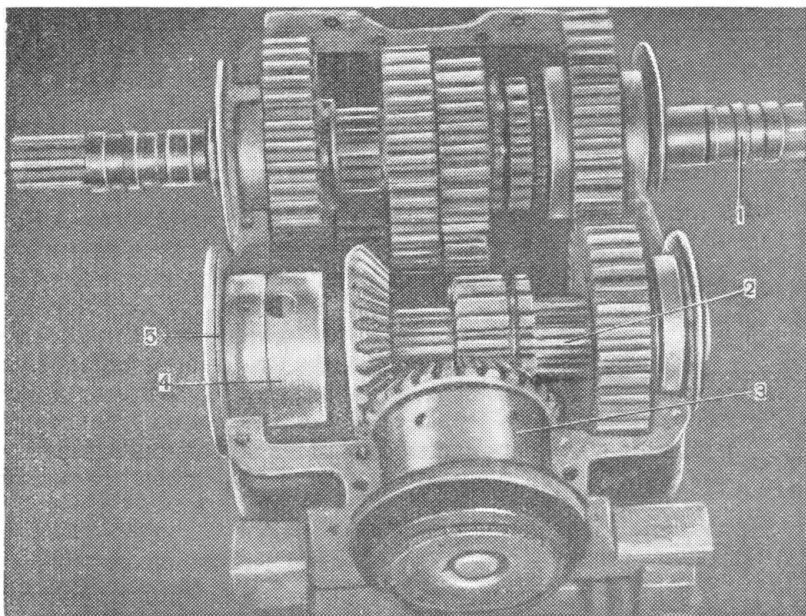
Нижняя половина картера 703-12-сб. 103 в сборе с валами:
